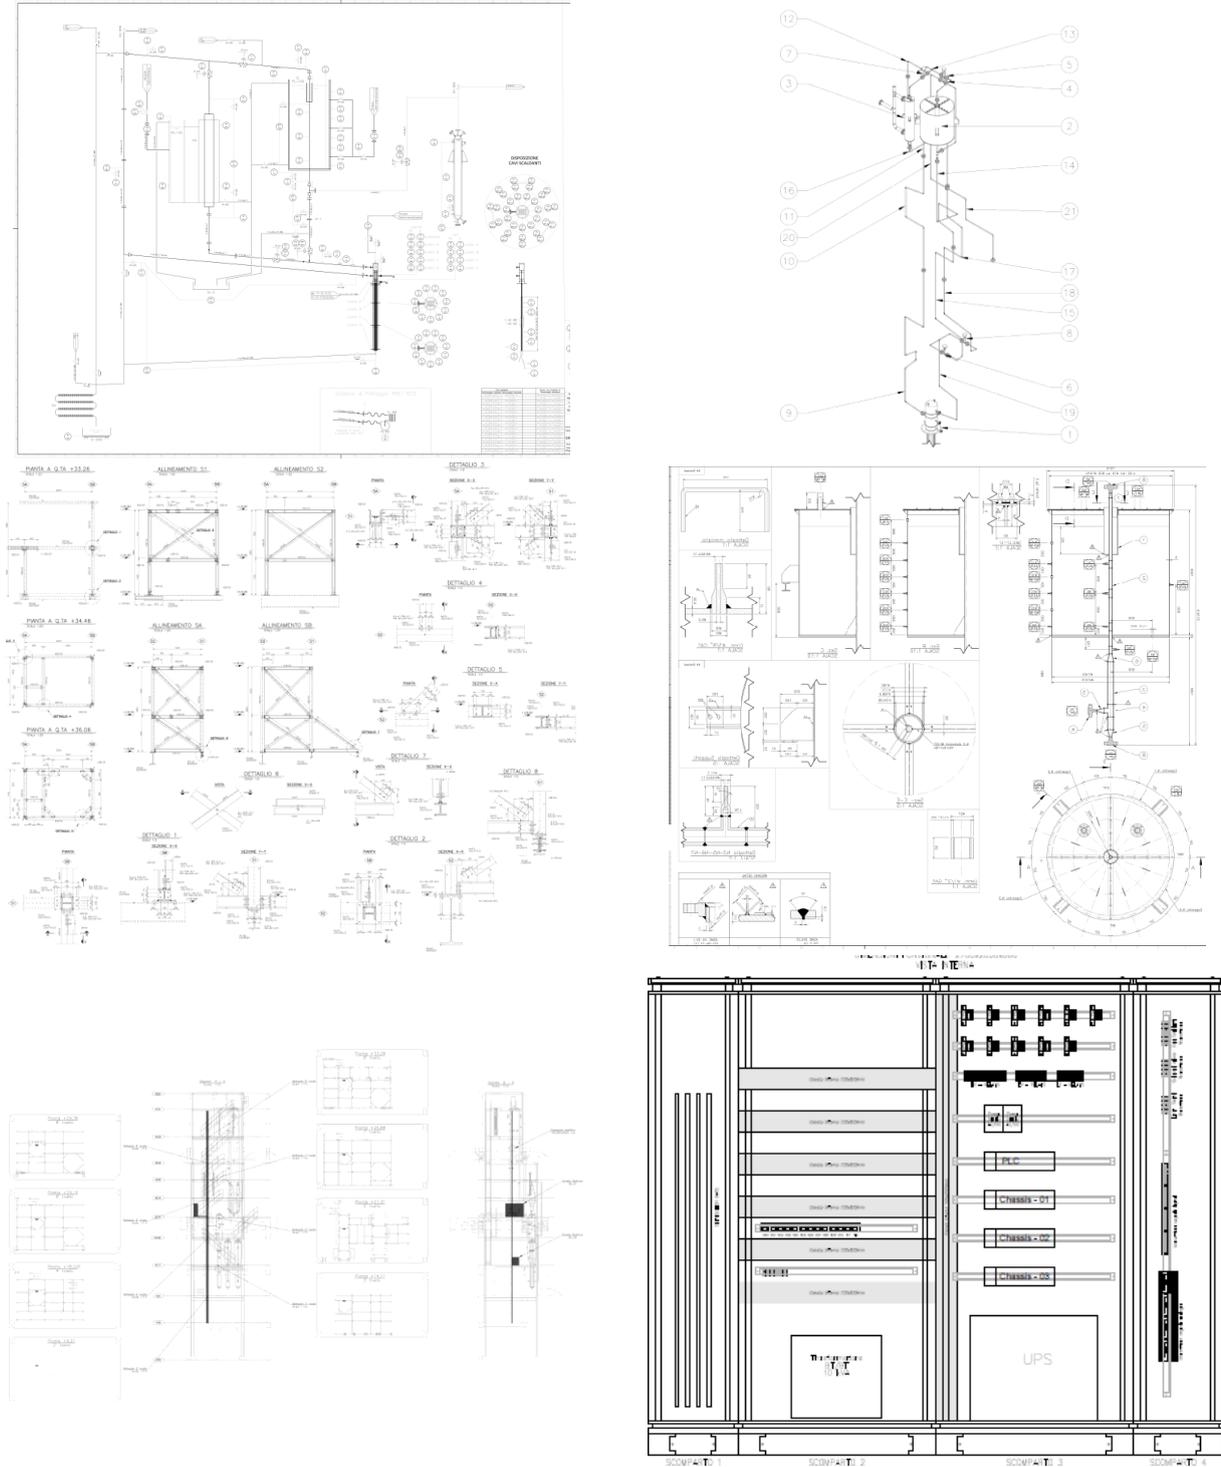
Immagini di elaborati di progetto - P&ID, layout, schemi e disegni.
